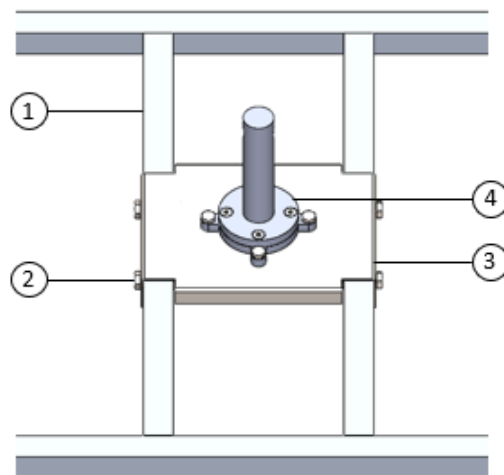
Ligação do conjunto de fixação do mastro ao chassi: 1 - Chassi; 2 - Ligação aparafusada; 3 - Chapa de fixação; 4 - Conjunto de fixação do mastro
